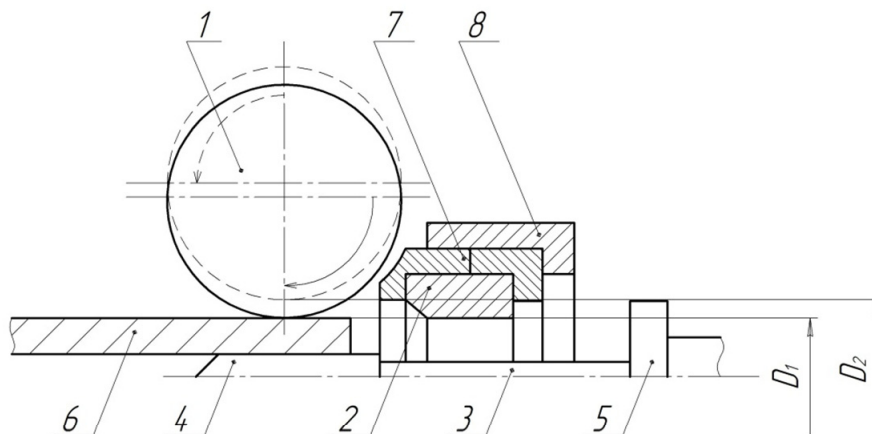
Схема устройства на стадии выпрессовки пресс-остатка:
